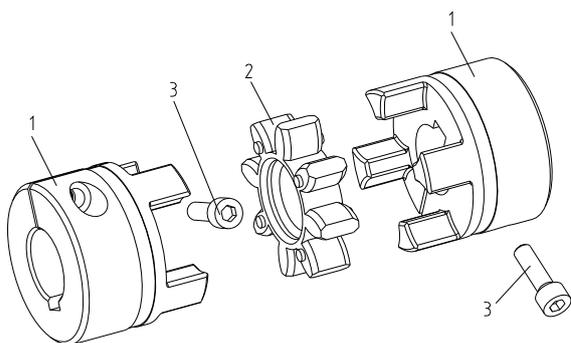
ROTEX® GS Compact, типоразмеры 7 - 19
